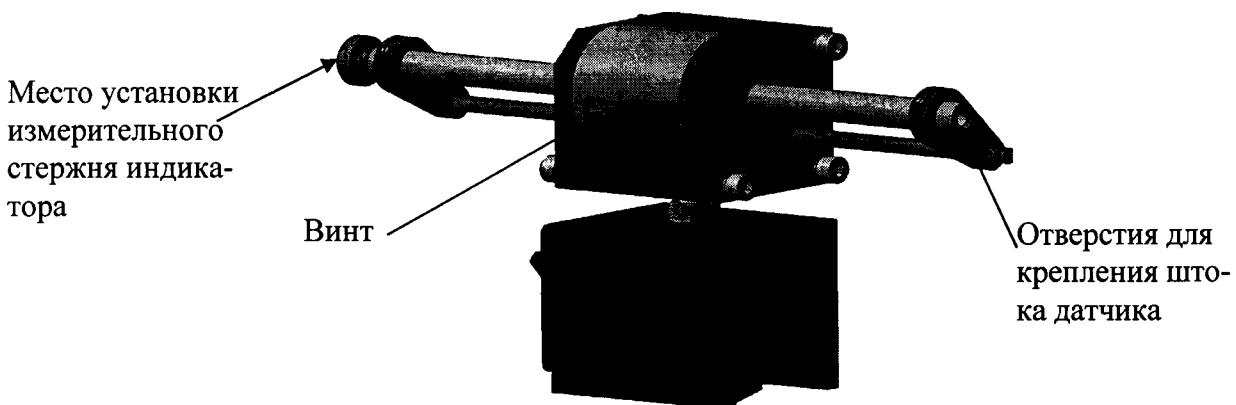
Специальное приспособление для поверки индуктивного датчика линейных перемещений
